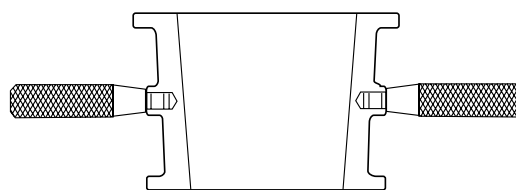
Конусный калибр для измерения конусности шейки прокатного вала
